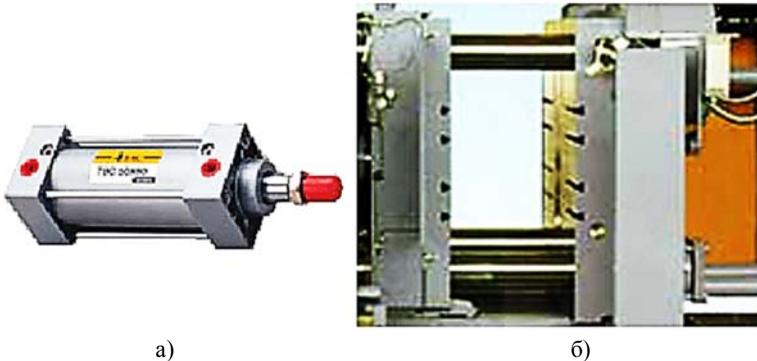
а) стандартный пневмоцилиндр выполняющий роль ресивера для создания *сжатого* воздуха; б) неподвижная и подвижная плиты горизонтальной с холодной камерой прессования литейной машины
